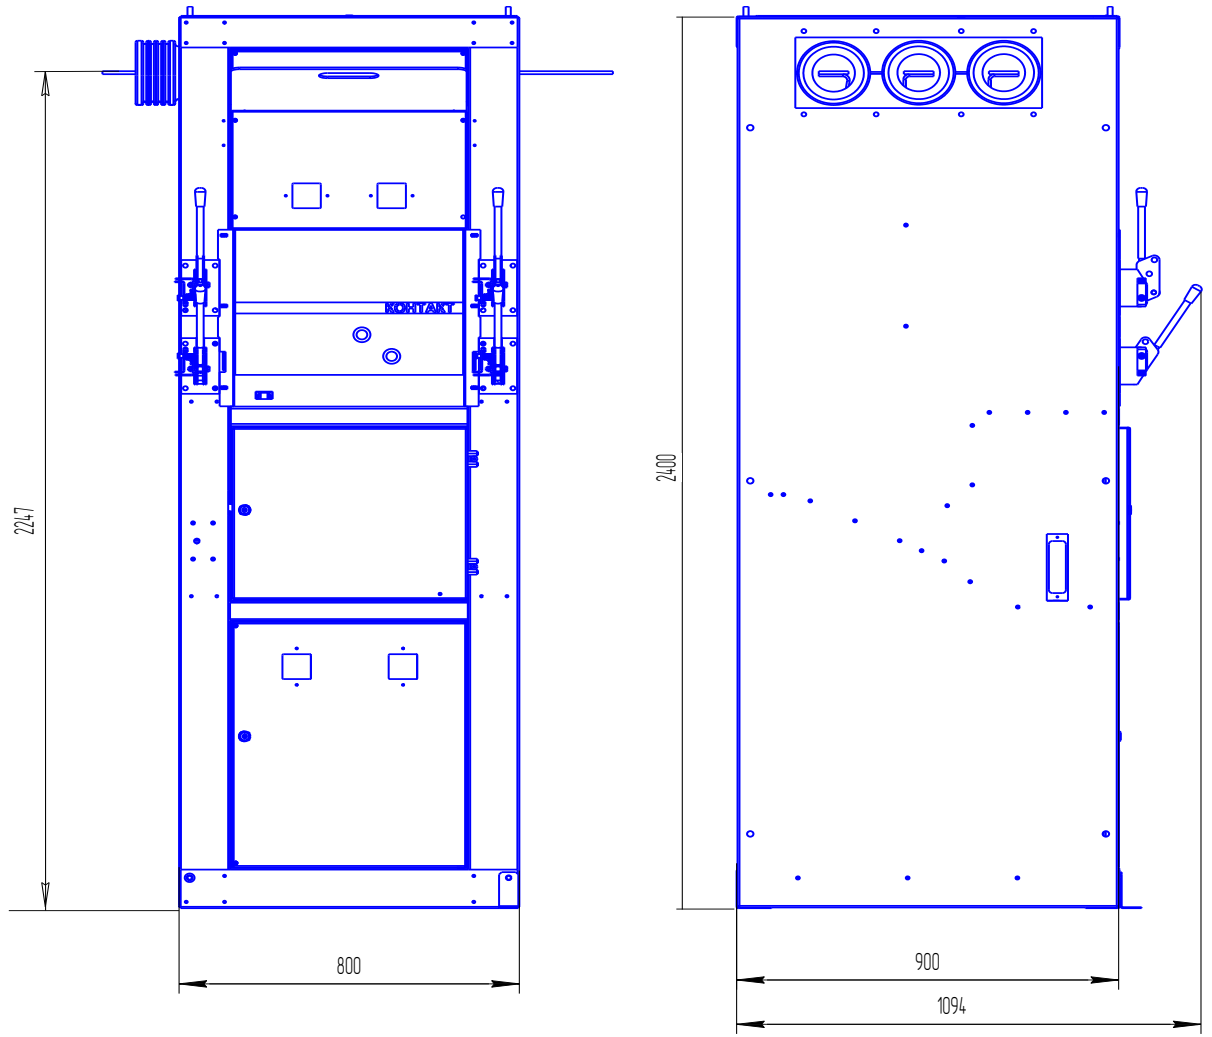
Габаритные размеры камеры КСО - 203 - 07
